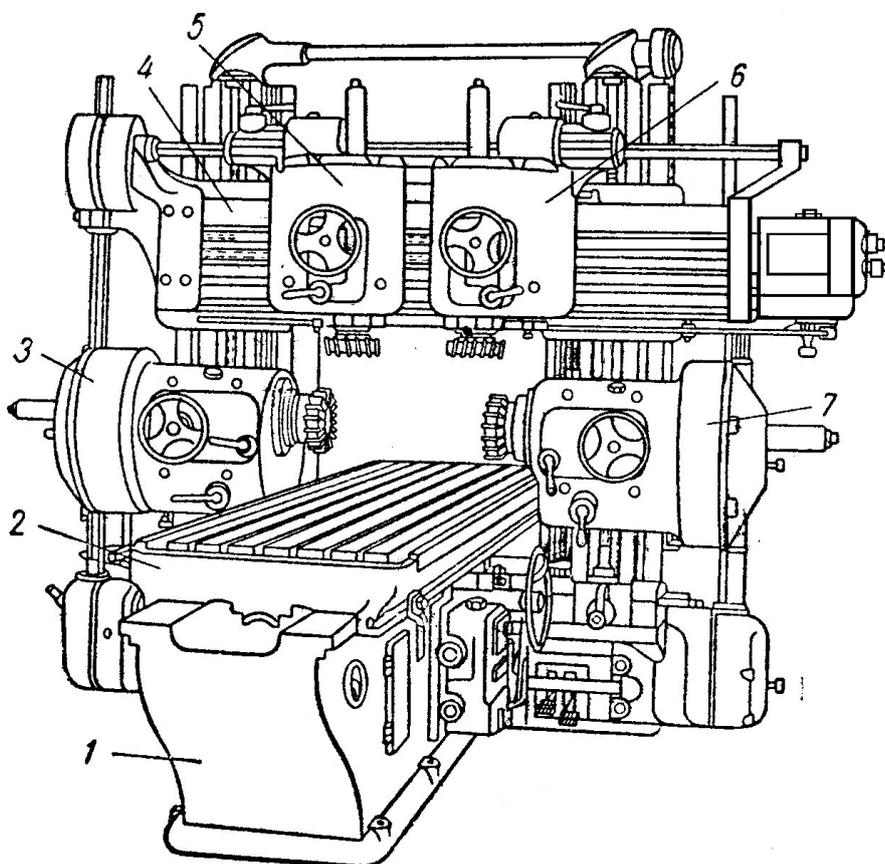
Общий вид четырехшпиндельного продольно-фрезерного станка: 1 – станина; 2 – стол; 3, 5, 6, 7 – шпиндельные бабки; 4 – поперечина
